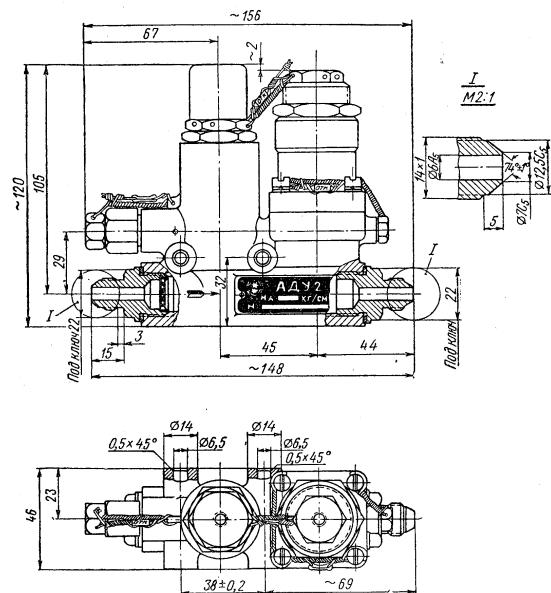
Клапан обратный (узел) АДУ2-03.
